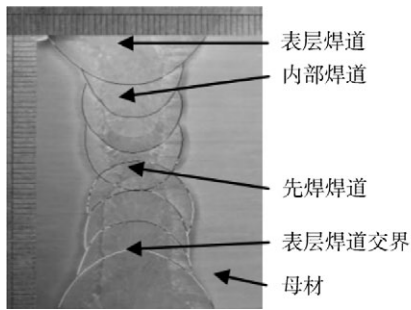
磁控窄间隙钛合金焊缝接头横截面宏观形貌
